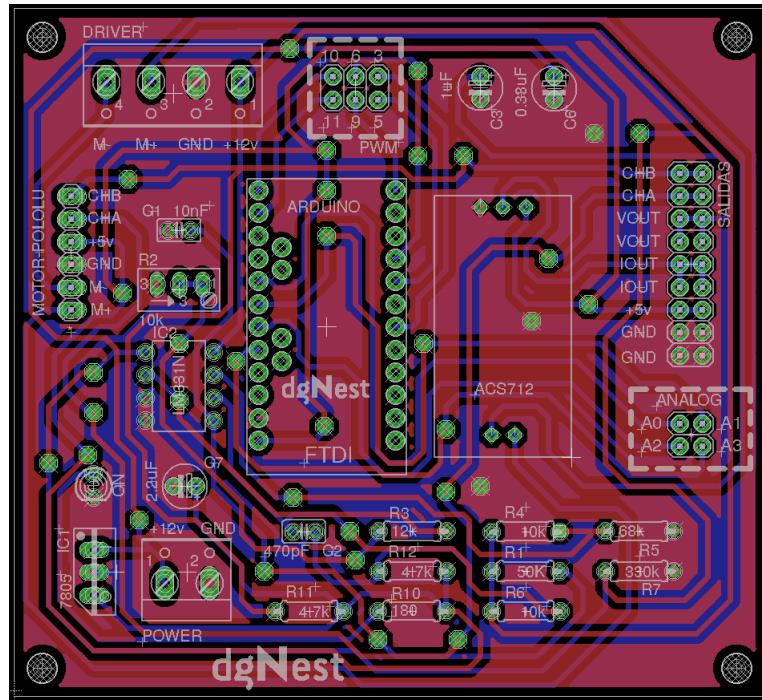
PCB (board) del circuito LM331 diseñado para un motor EMG30
